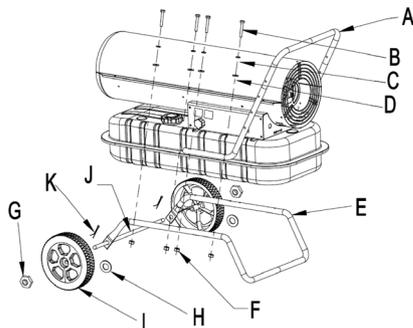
Внешний вид Hintek DIS 30, DIS 50, DIS 70, DIS 100
